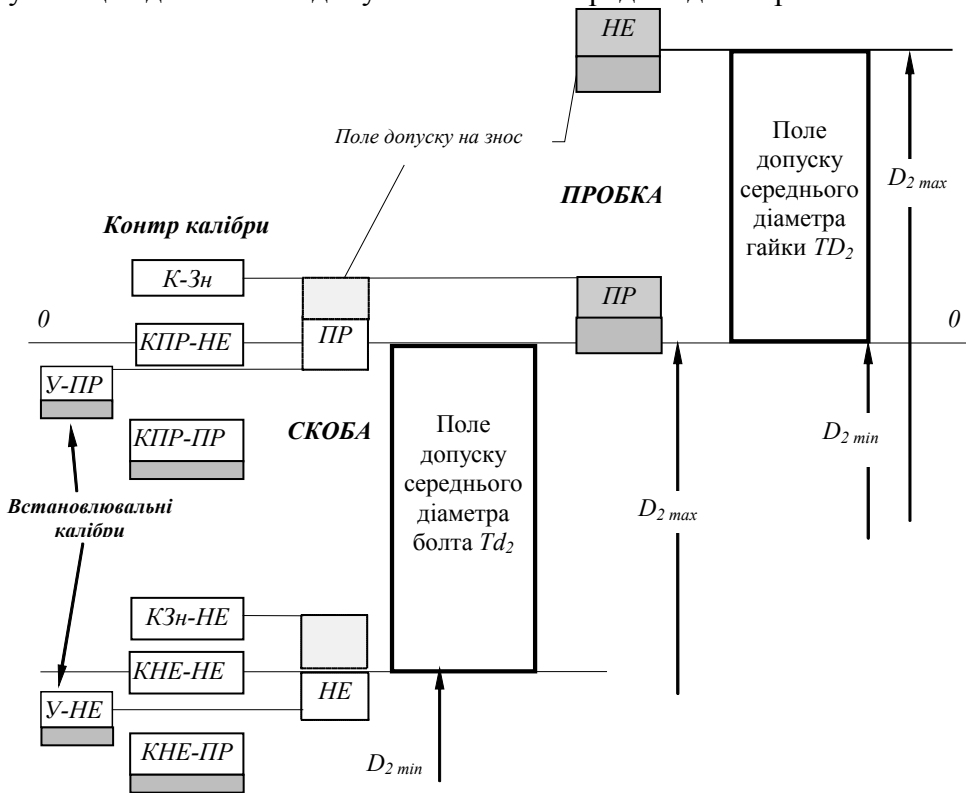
Схема розташування полів допусків різьбових калібрів для контролю поля допуску середнього діаметра
